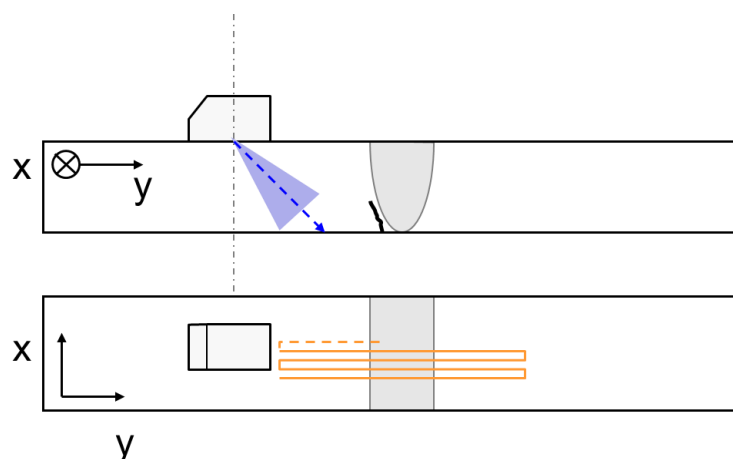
Schema der mechanisierten Ultraschallprüfung an austenitischen Schweißnaht-Testkörpern (oben: Seitenansicht; unten: Draufsicht).
